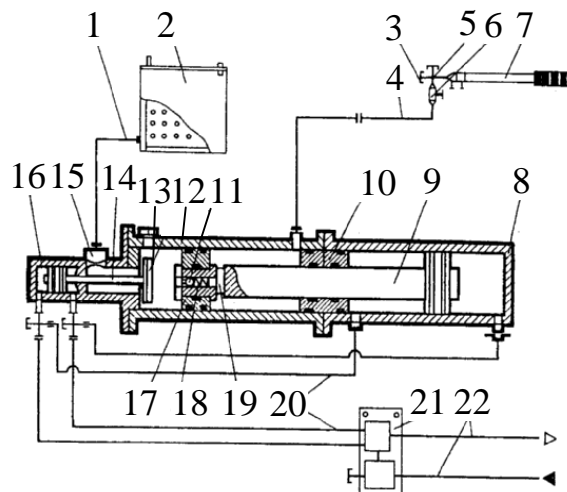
Принципова схема установки УНР-1 під час нагнітання карбамідного скріплювального складу: 1 – рукав; 2 – ємність з фільтром; 3 – муфта; 4 – рукав; 5 – хрестовина; 6 – кран; 7 – герметизатор; 8 – силовий циліндр; 9 – поршень; 10 – грундбукса; 11 – зворотний клапан; 12 – нагнітальний гідроциліндр; 13 – клапан примусового відкриття зі стеком 14; 15 – усмоктувальний патрубков; 16 – додатковий циліндр; 17 – поршень із гніздом 18; 19 – канал; 20 – рукава; 21 – блок керування; 22 – високонапірні рукава
